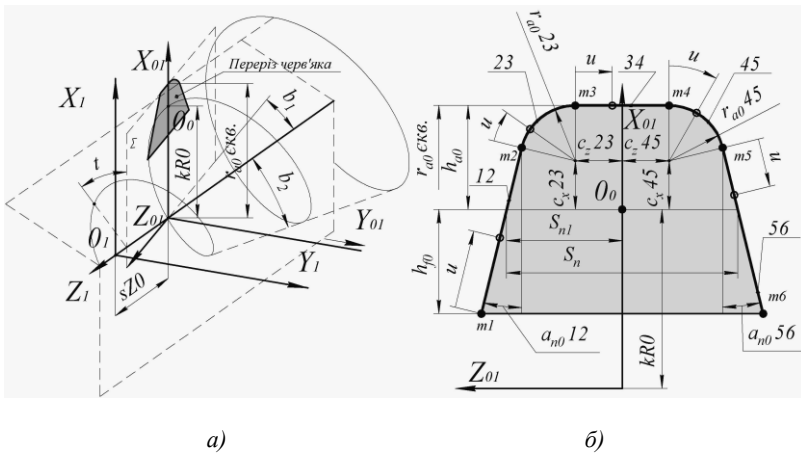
Схема утворення ВІП конічної черв'ячної фрези:
